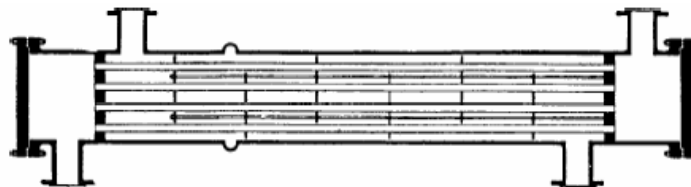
Intercambiador con cabezal de tubos fijo con carretes integrales. (Patterson Foundry & Machine Co.)
